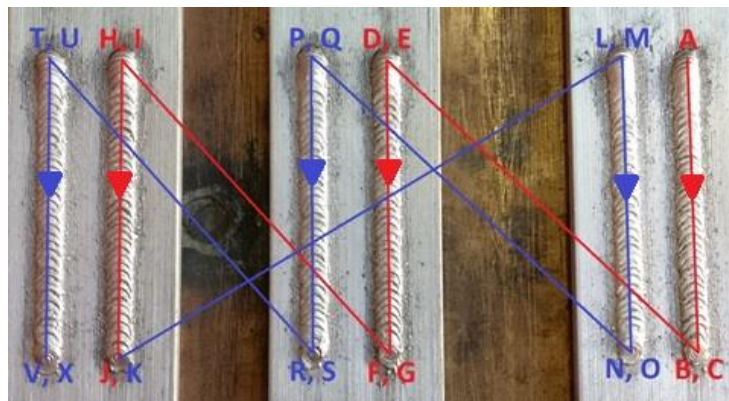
Esquemática da trajetória de deslocamento e soldagem.
